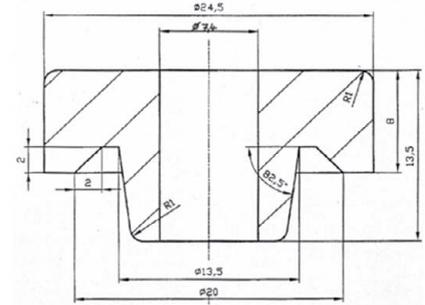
Pilzkopfdichtung (Vibra-Dichtung, siehe auch Anlage 2, Blatt 7, Bild 2.13)
